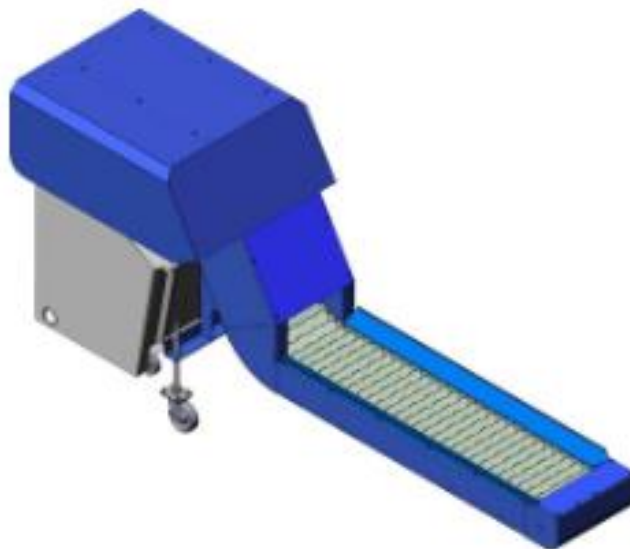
Транспортёр для видалення стружки з верстата фірми HAAS
